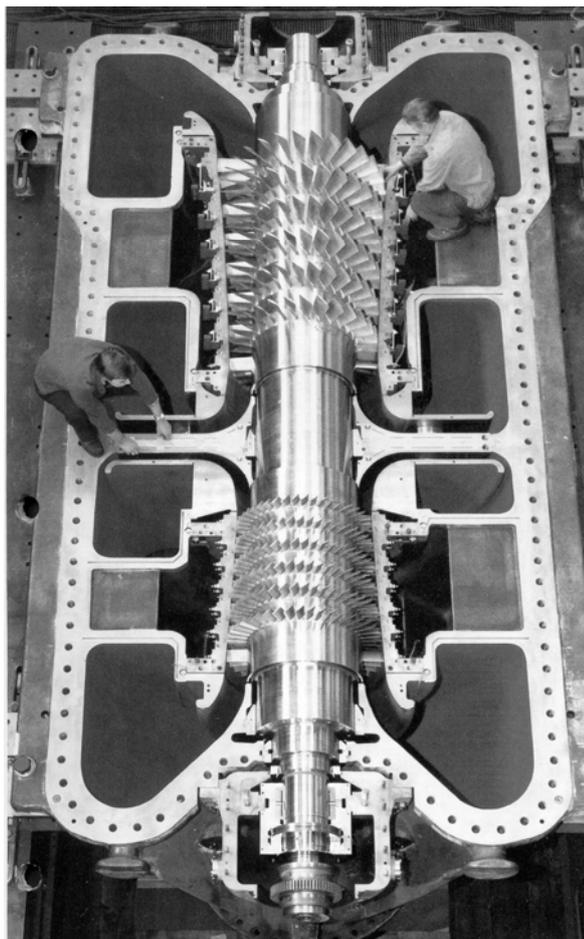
Двухсекционный осевой компрессор промышленного назначения (верхняя часть корпуса снята)
